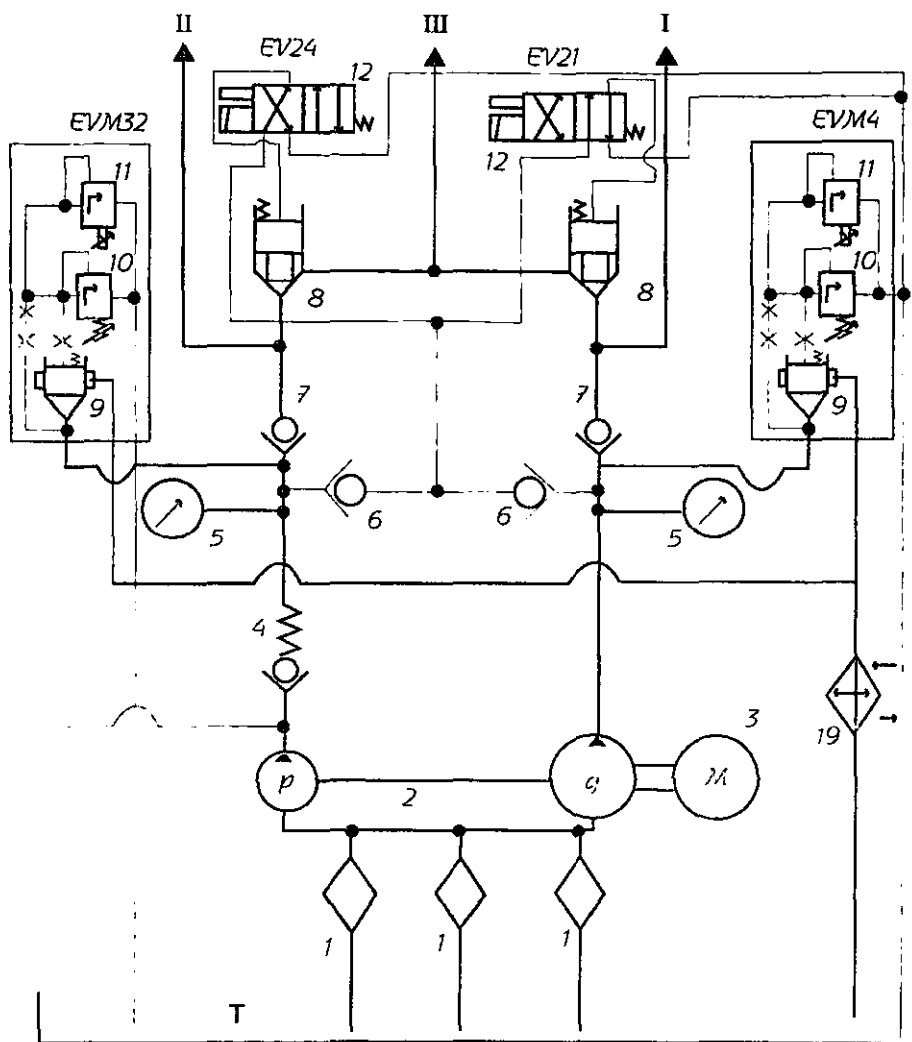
Grupo para el cierre de moldes por la bomba grande.
